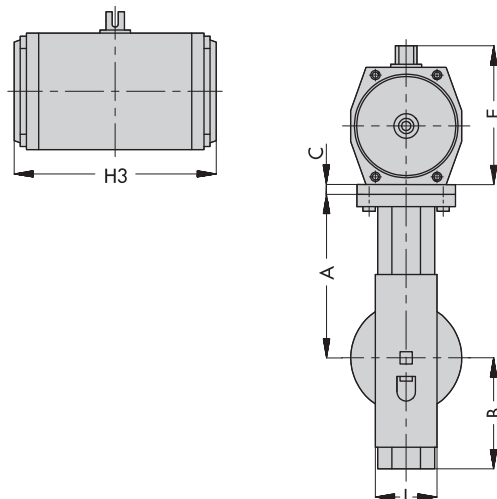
· Dimensions pour vanne papillon type 3335/BR 31a
